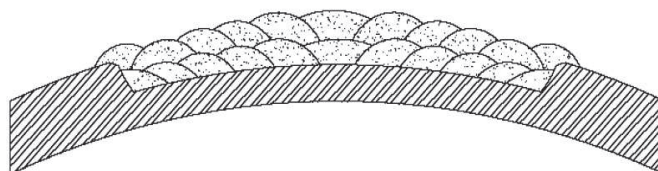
Depósito de material (soldadura), en un defecto de corrosión externa ^[5].
